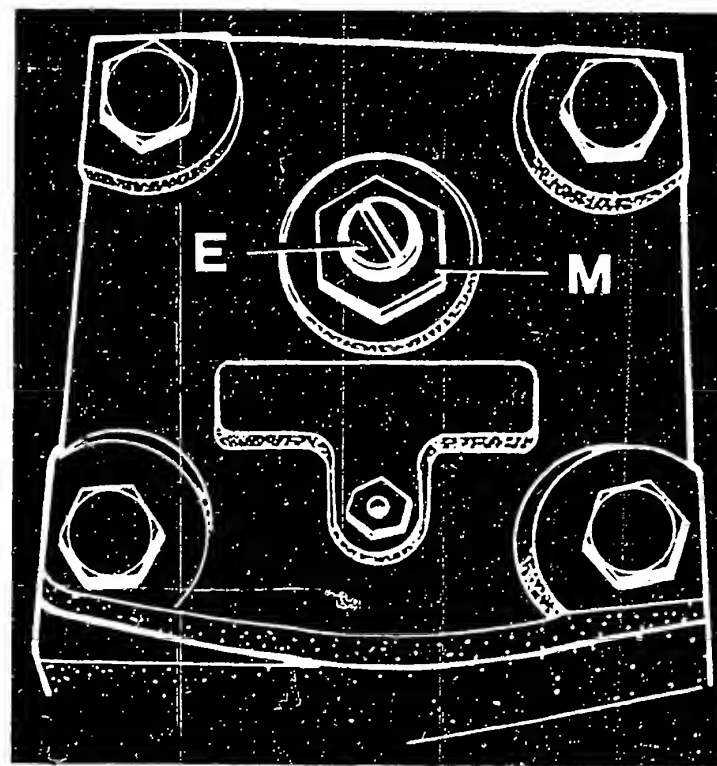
Einstellschraube E des Lenkgetriebes. Die Kontermutter M wird mit 27Nm befestigt.
